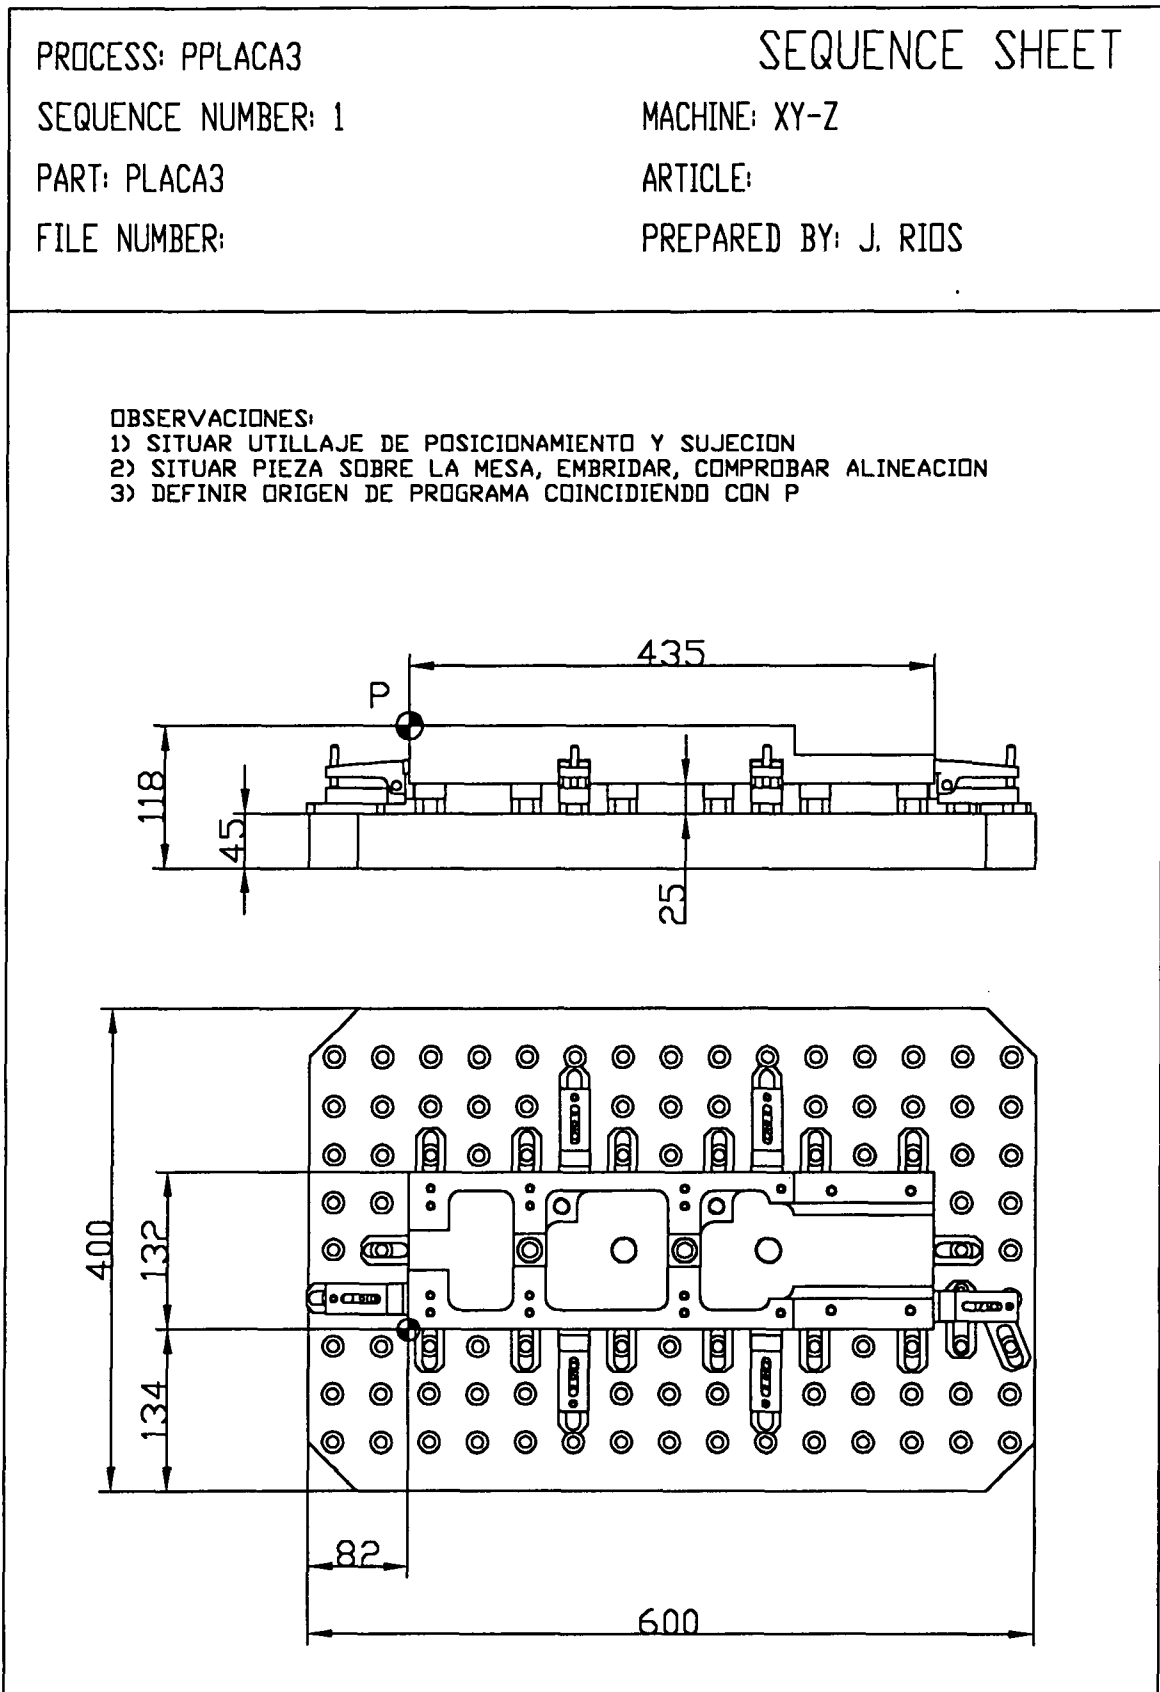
Croquis de disposición en máquina de la pieza: placa 3.
